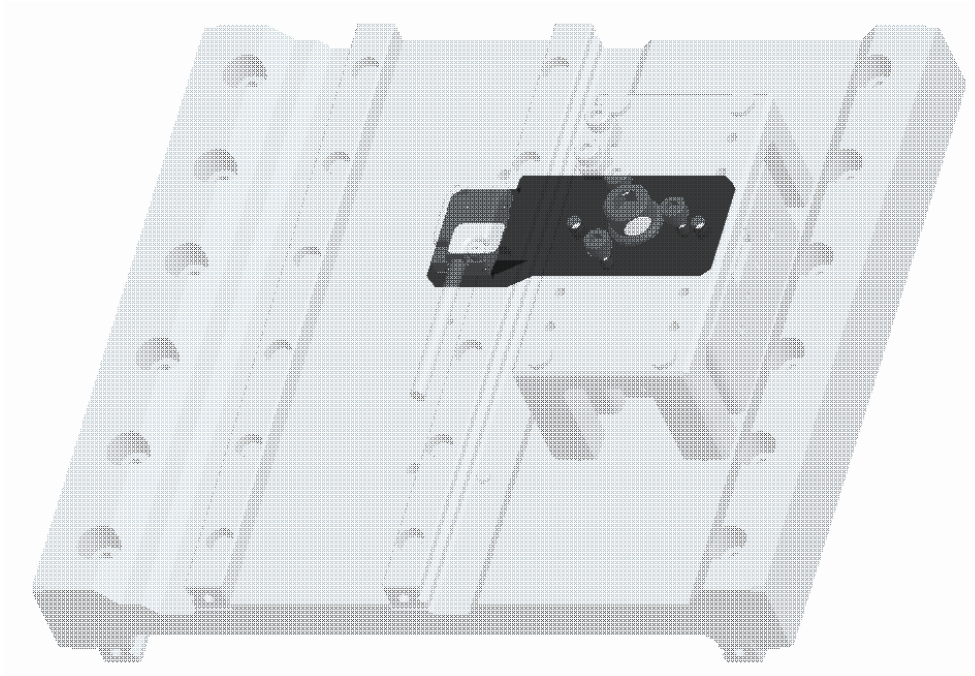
Halterung Encoder Oben ⇔ Mitte
